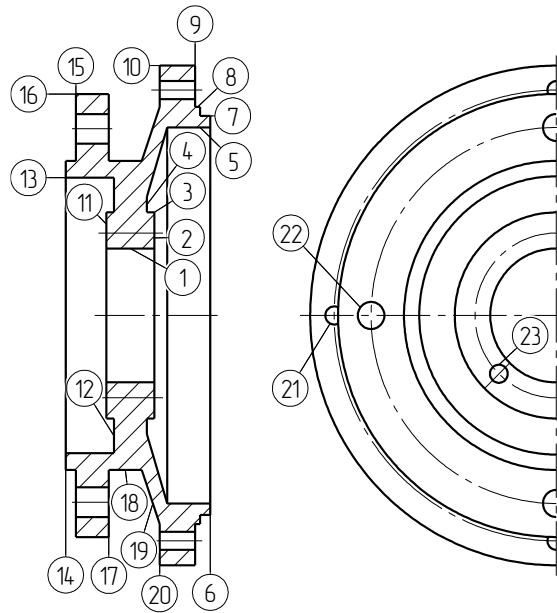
Ескіз деталі з номерами поверхонь
